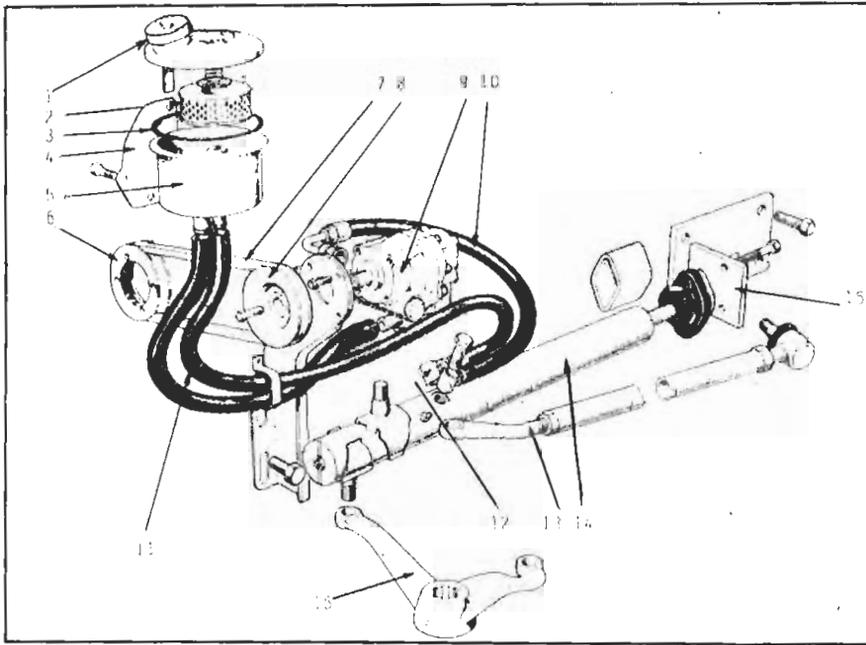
Despiece de una dirección ayudada. 1.- Tapón para el llenado de aceite. 2.- Filtro. 3.- Junta. 4.- Soporte. 5.- Depósito. 6.- Polea del cigüeñal. 7.- Correa. 8.- Polea de la bomba. 9.- Bomba. 10.- Latiguillo de impulsión. 11.- Id. de retorno. 12.- Conexión del latiguillo. 14.- Cilindro hidráulico de doble efecto. 15.- Palanca. 16.- Soporte de fijación del vástago al bastidor.
